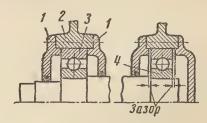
Подшипниковые узлы на шарикоподшипниках.
